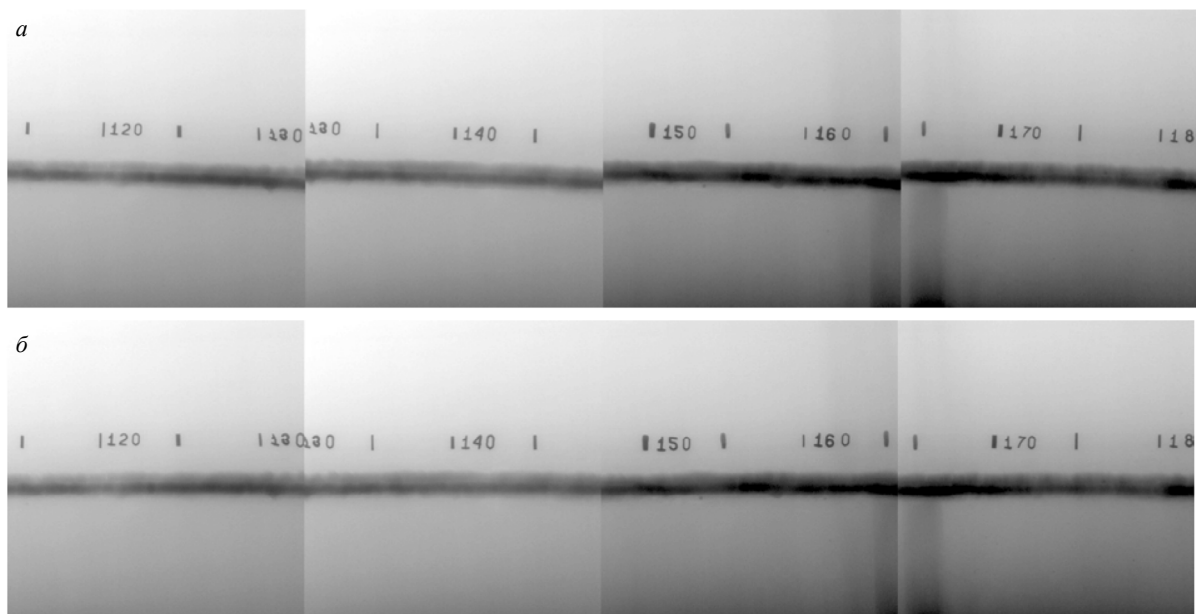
Негоризонтальная ориентация сварного шва:
